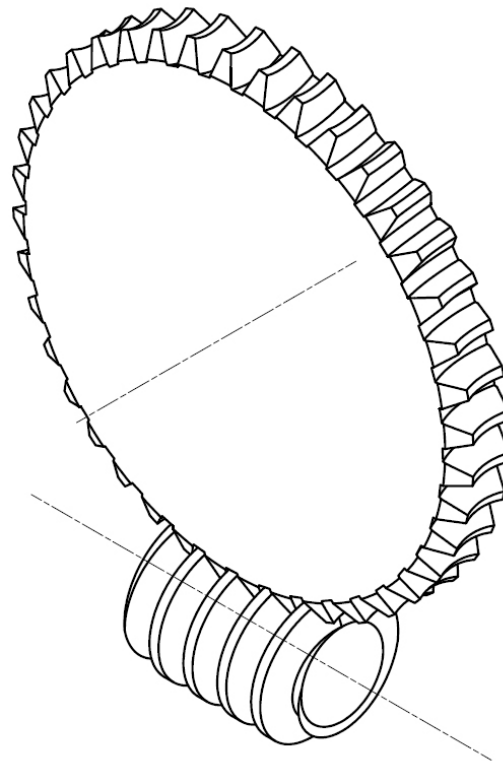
Engranaje de Tornillo Sin Fin - Rueda
